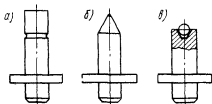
Формы концов осей для шарикоподшипников без внутренних колец
